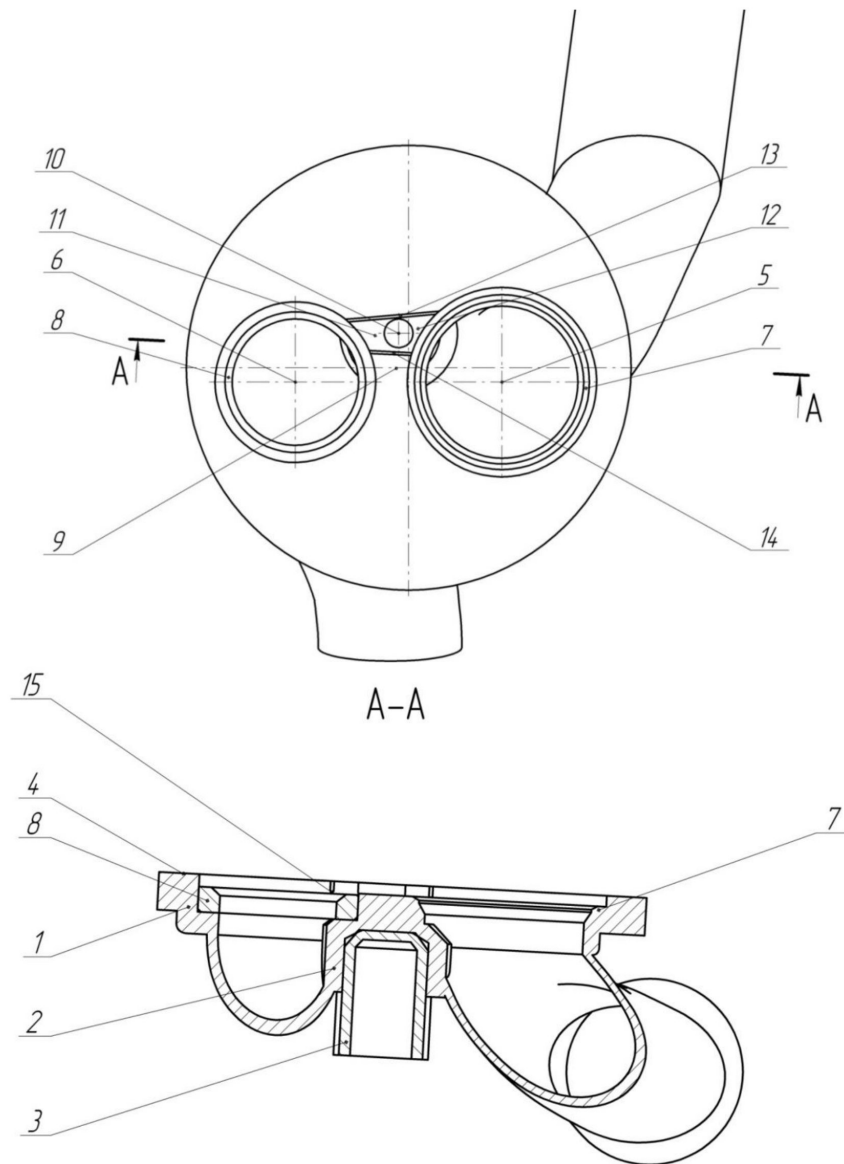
Принципова схема розміщення деконцентраторів напружень: 1 – корпус головки блоку циліндрів; 2 – прилив (бобишка), 3 – форсунковий стакан; 4 – вогневе днище головки блоку циліндрів; 5 і 6 – клапанні отвори під впускний і випускний клапани відповідно; 7 і 8 – клапанні гнізда під впускний і випускний клапани, відповідно; 9 – міжклапанна перемичка; 10 – форсунковий отвір; 11 – перемичка між форсунковим отвором 10 і випускним клапаном 5 (область найбільш ймовірного виникнення термовтомних тріщин); 12 – перемичка між форсунковим отвором 10 і випускним клапаном 6; 13 і 14 – термокомпенсаційні прорізи, які розташовані в області міжклапанної перемички 9; 15 – місце заокруглення країв деконцентратора
